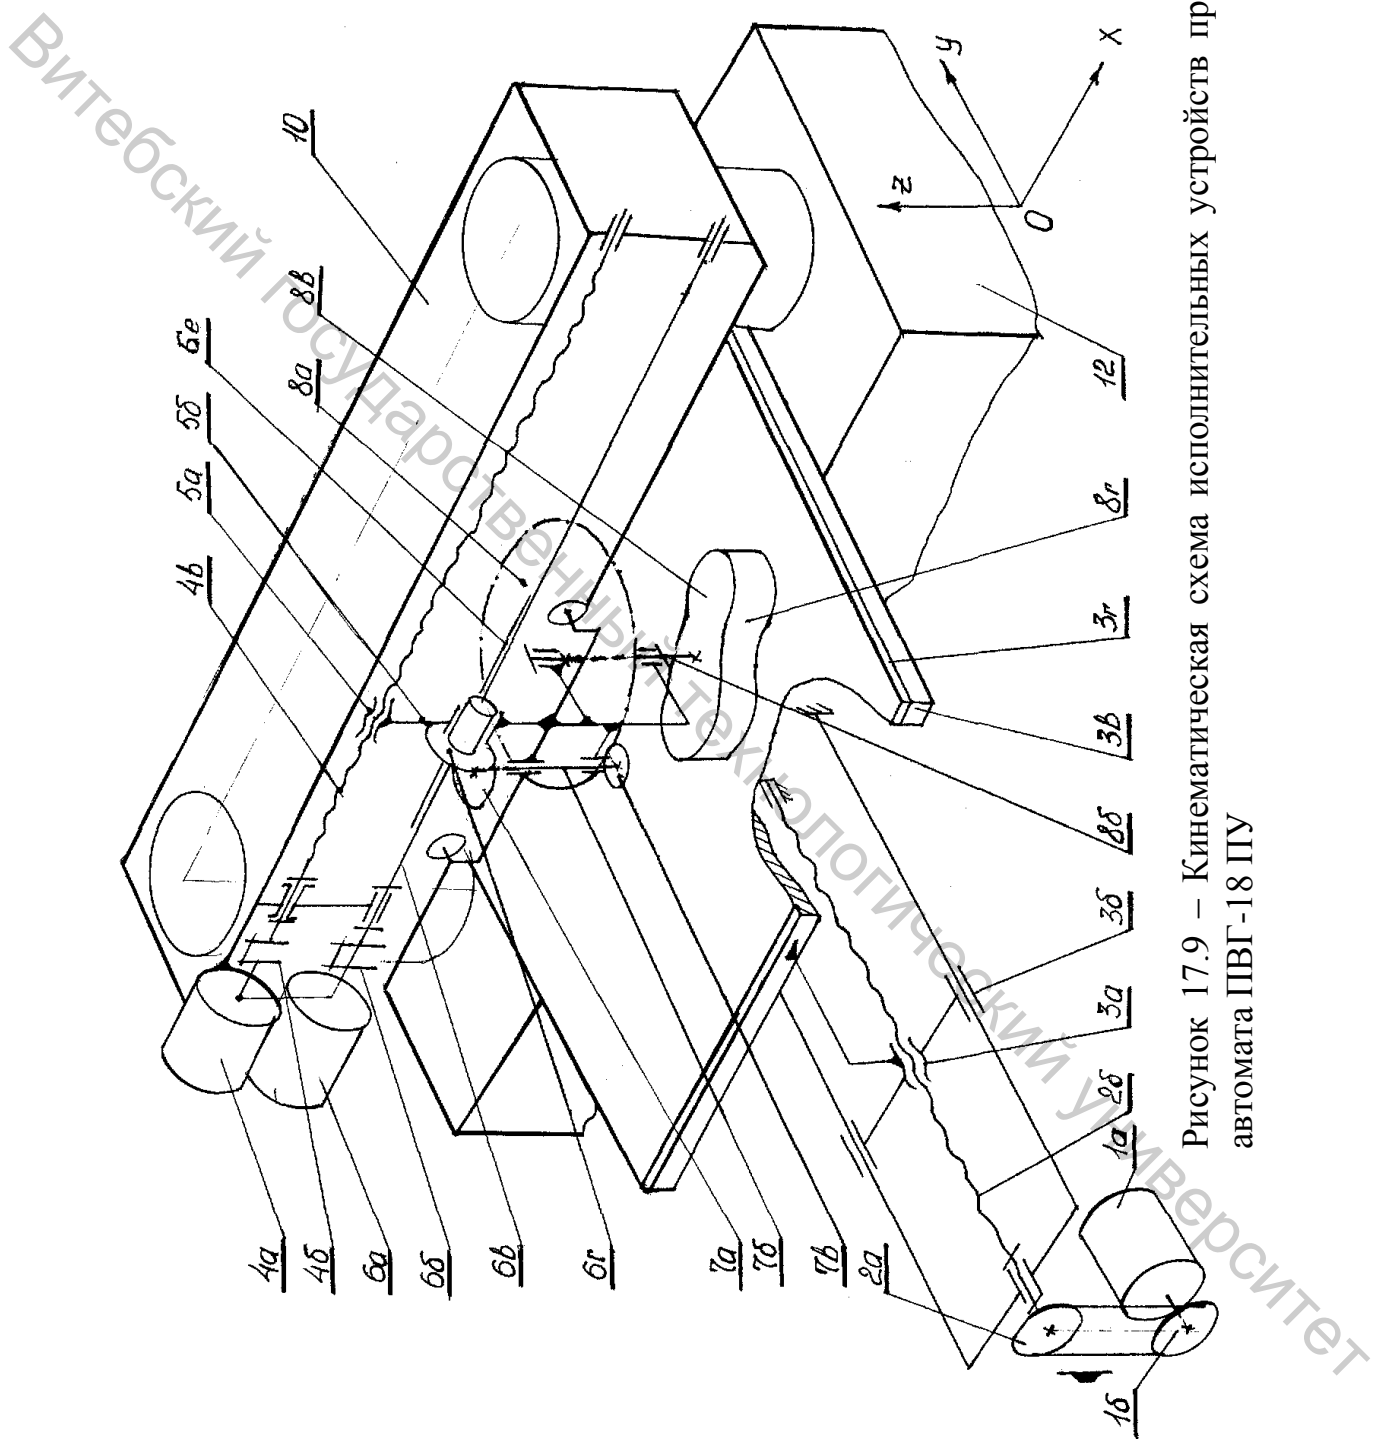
Кинематическая схема исполнительных устройств пресс-автомата ПВГ-18 ПУ
